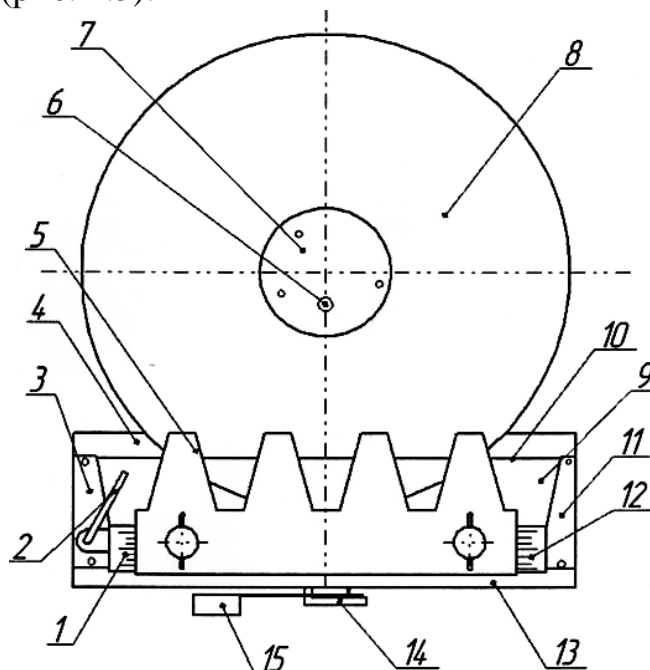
Прибор для построения эвольвентного профиля зуба
